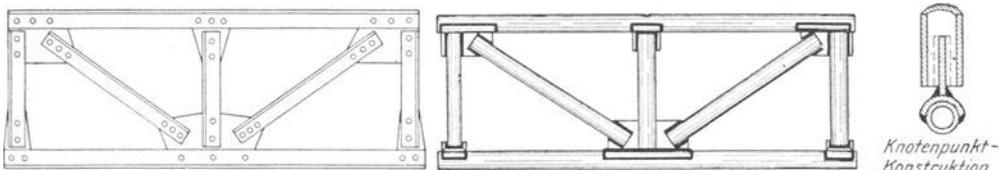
Genietete Winkeleisenkonstruktion ersetzt durch geschweißte Rohrkonstruktion.
